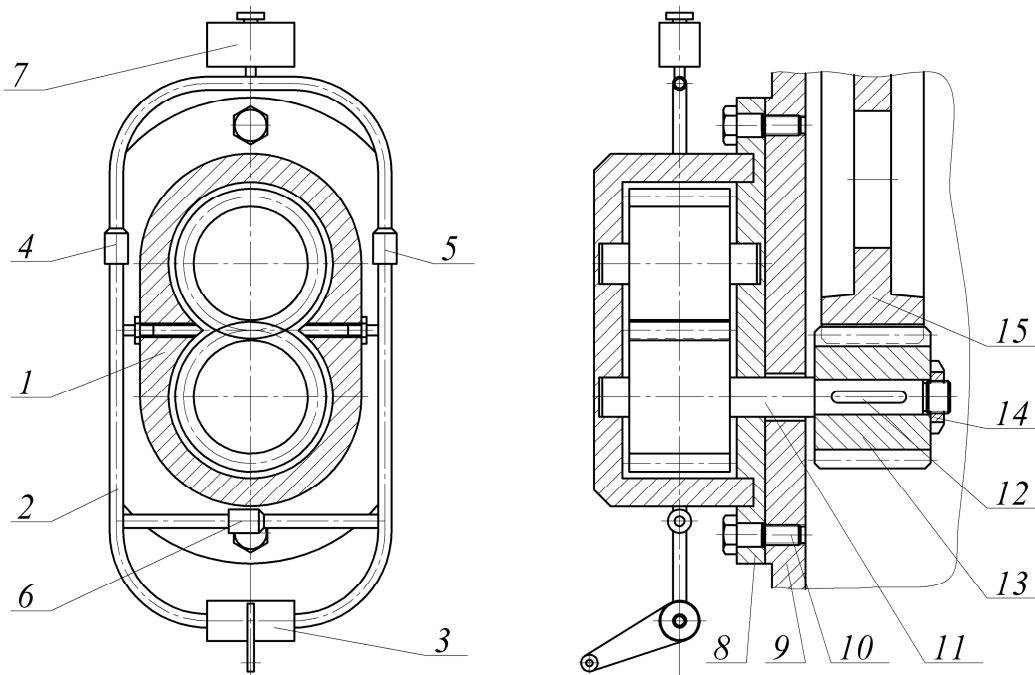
Конструктивна блок-схема установки вантажоупорного зупинника на редукторі механізму підйому вантажу
